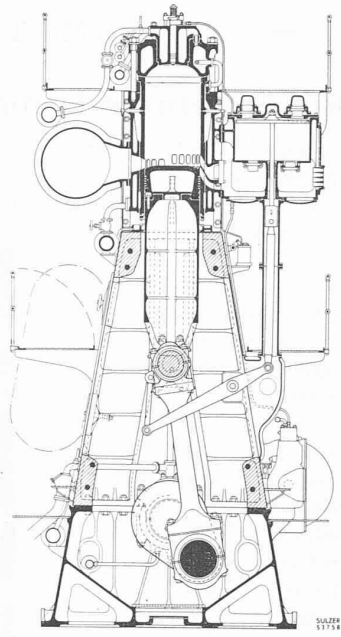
Coupe transversale schématique du moteur type «SD», modèle standardisé depuis 1945. La jupe du piston descend jusqu'à la crosse tandis que la séparation entre cylindre et carter est réalisée par une lanterne ouverte à l'air libre disposée au sommet du bâti.
